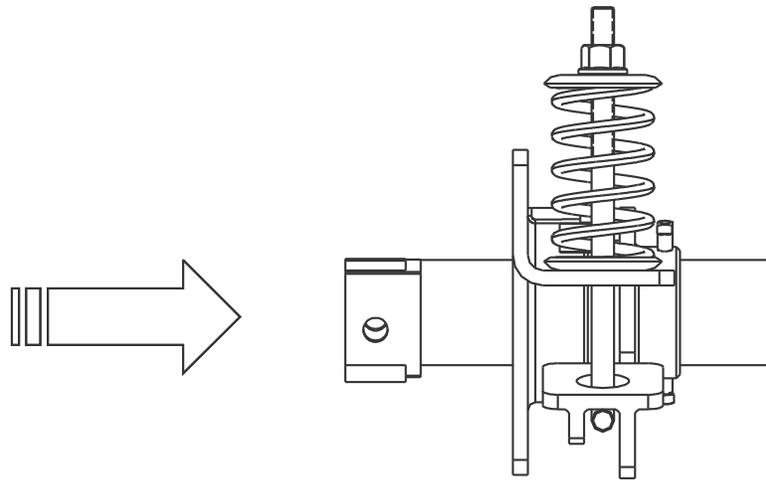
Inserte el Sostenedor del Tubo Dentro del Collar del Tensor (Ambos lados, Derecho e Izquierdo)
